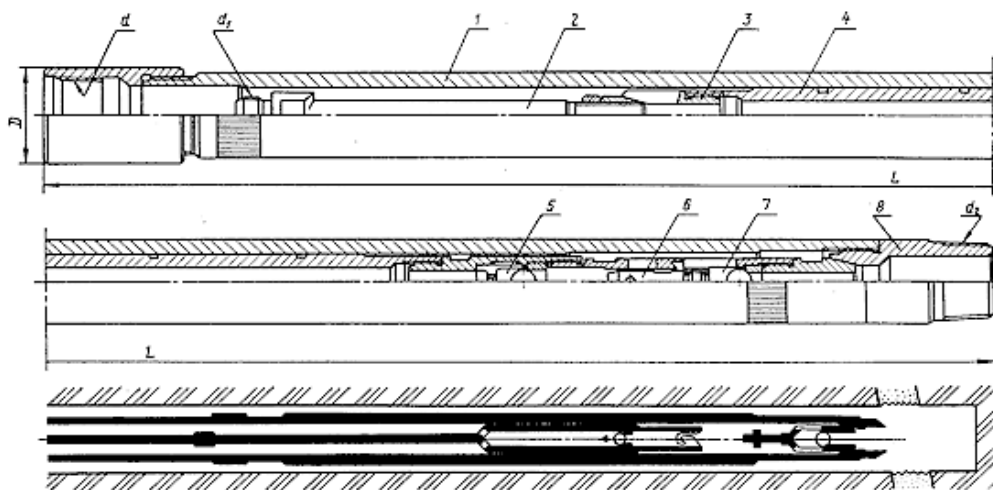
Насос ШГН: 1 - цилиндр; 2 - шток; 3 - клетка плунжера; 4 - плунжер; 5 - нагнетательный клапан; 6 - шток ловителя; 7 - всасывающий клапан; 8 - седло конуса;
